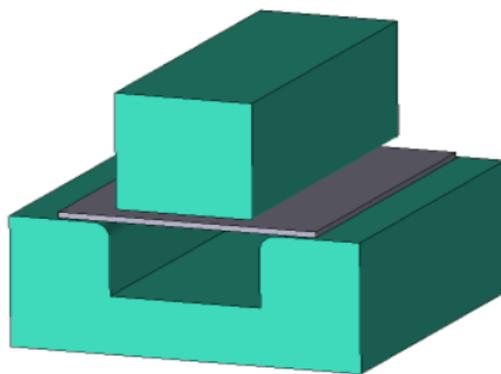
Побудовані моделі інструменту та заготовки для моделювання
